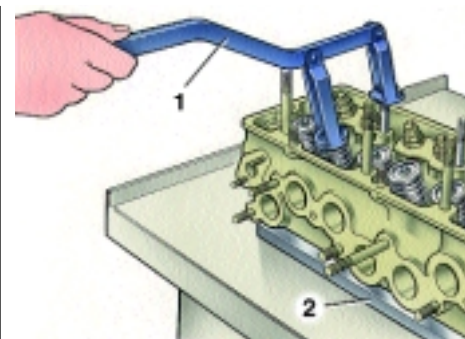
Снятие пружин клапанов двигателя мод. 2106-70: 1 – приспособление; 2 – монтажная доска
